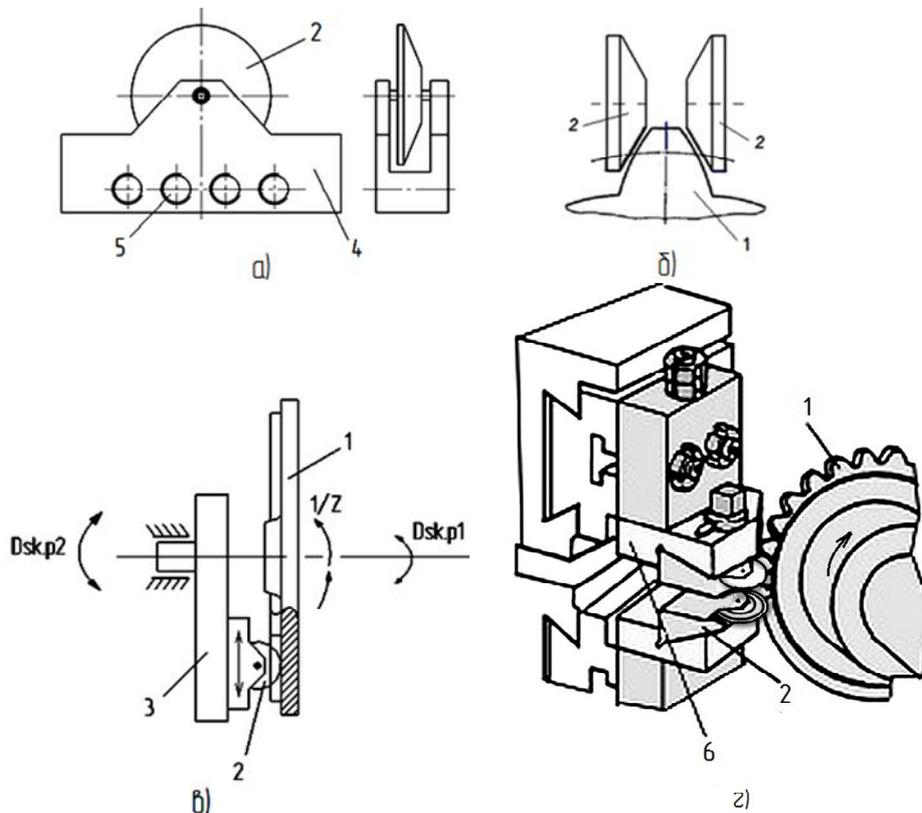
Схемы установки и накатывания: 1 – накатываемое зубчатое колесо, 2 – накатной ролик, 3 – люлька, 4 – державка, 5 – отверстия для крепления к ползуну, 6 – ползун
